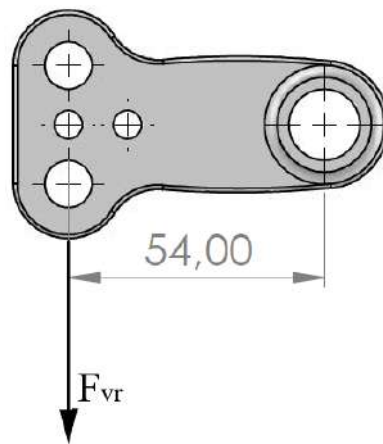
Distancia entre la columna de dirección con la unión del varillaje en mm
